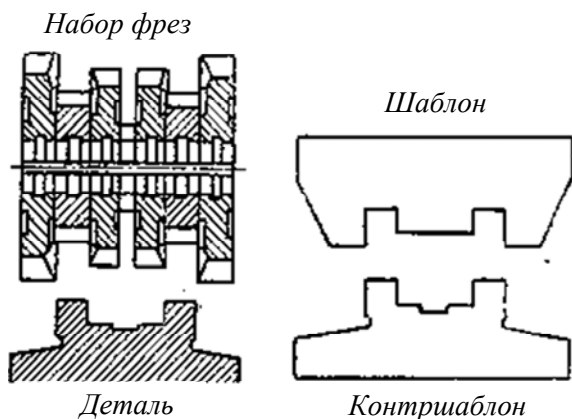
Набор фрез, деталь, шаблон и контршаблон
